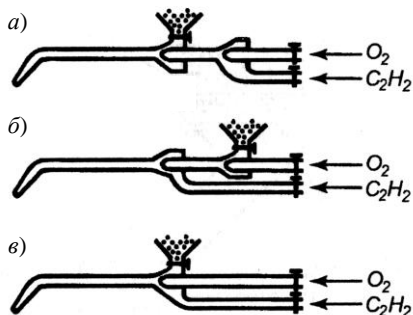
Схема горелки для газопорошковой наплавки: 1 – бункер с порошком; 2 – канал для подачи кислорода; 3 – канал для подачи горючего газа
